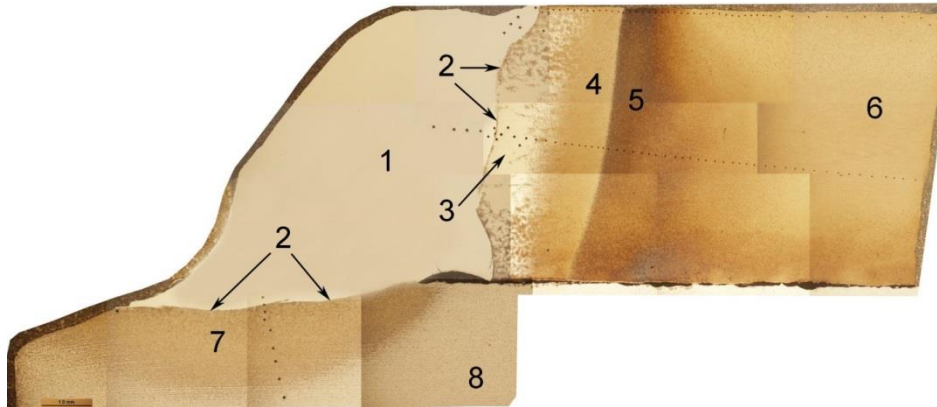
Зварне з'єднання загартованої сталі 120Г3С2 і сталі 09Г2С.
